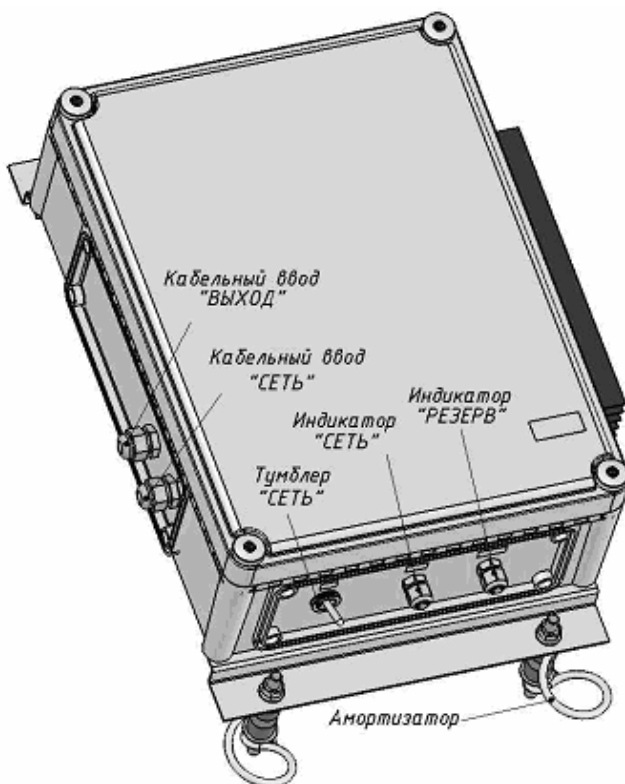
Общий вид блока бесперебойного питания ВОЛНА ББП-3/20 исп.5
